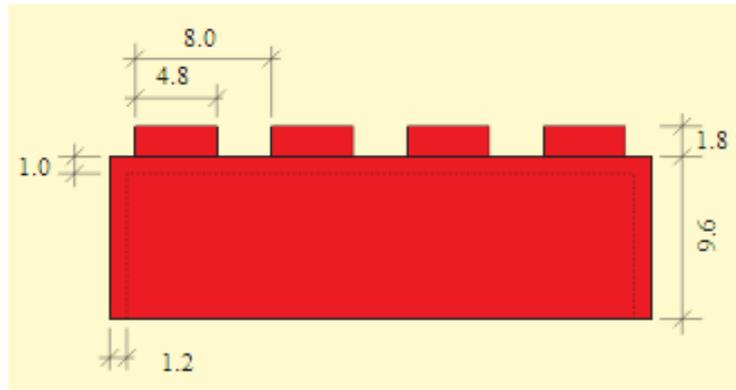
Vista lateral izquierda de una pieza de LEGO 4x2.
